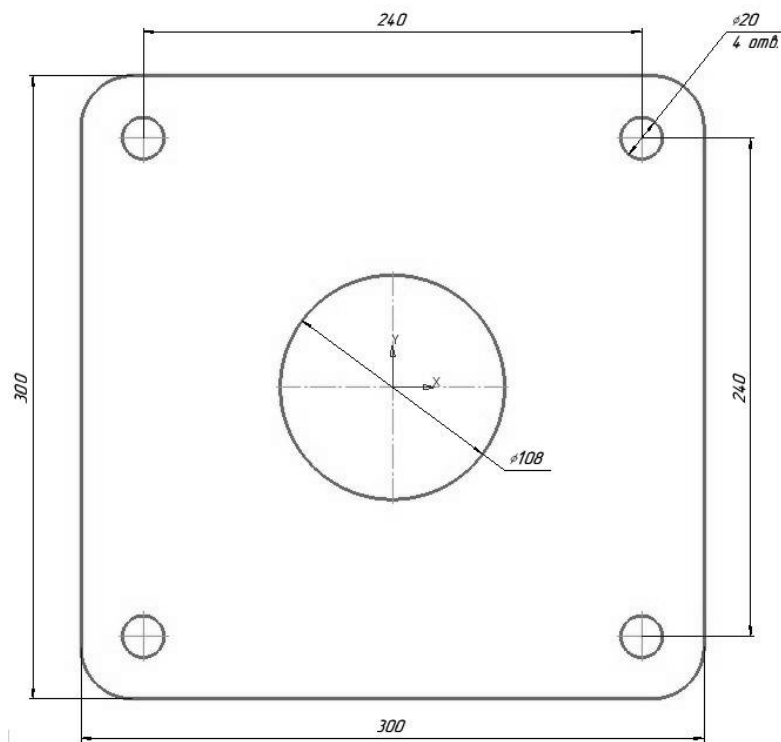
Внешний вид и габаритные размеры светильника
